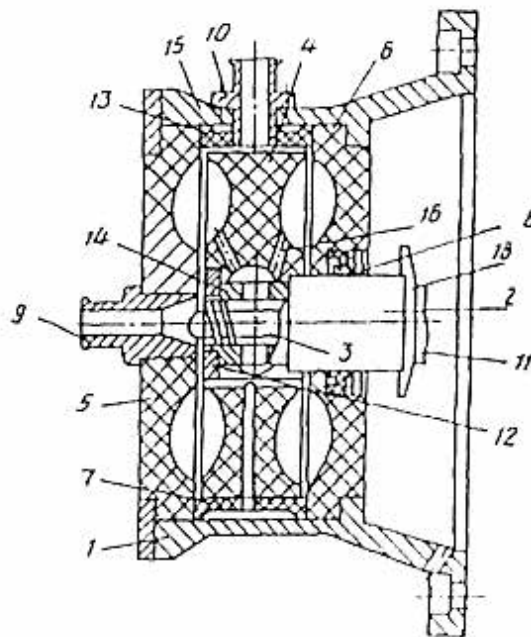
Гідродинамічний нагрівач рідини серійної установки ПМР-02: 1 – корпус; 2 – вал; 3 – осьовий насос; 4 – ротор; 5,6 – кришки; 7 – кільце; 8 – ущільнювальна манжета; 9 – вхідний патрубок; 10 – випускний патрубок; 11 – електродвигун; 12 – гайка; 13, 14, 15 - гумові кільця; 16 – канали, що подають молоко.
